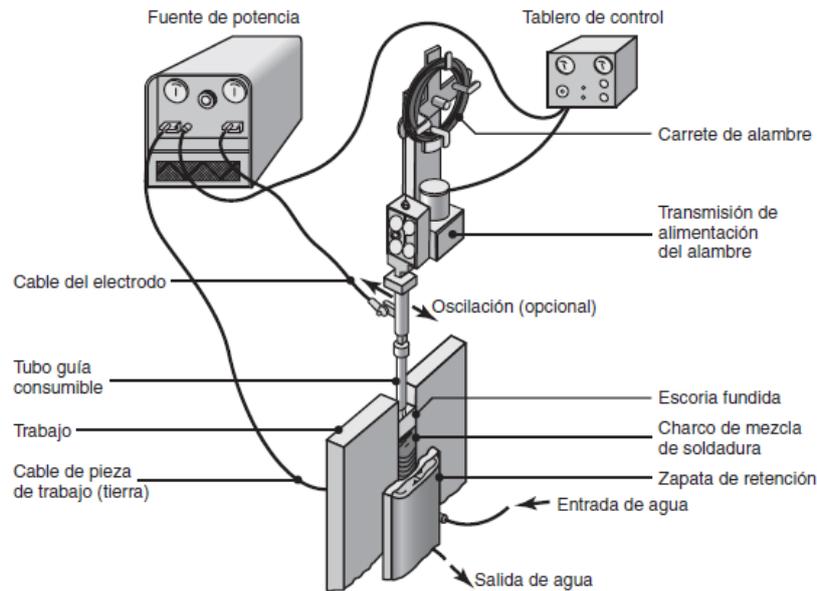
Esquema de la soldadura con electroescoria (Fuente: *Manufactura, Ingeniería y Tecnología*)
